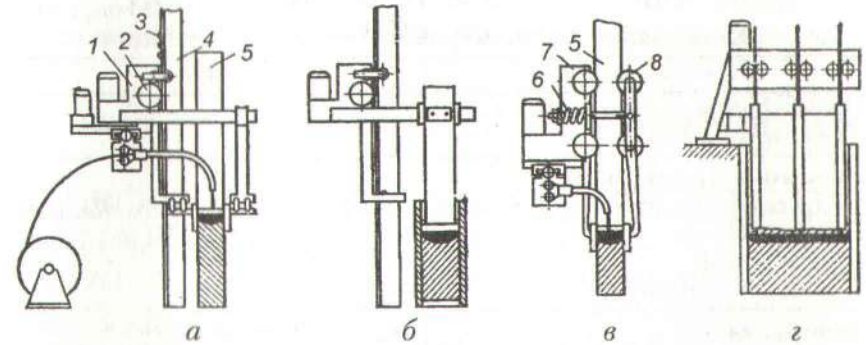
Принципові схеми будови апаратів для електрошлакового зварювання:
